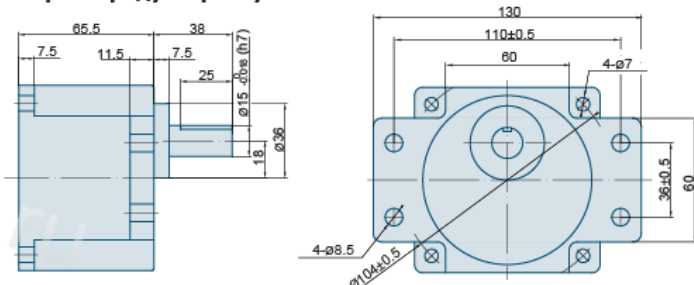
Редукторный электродвигатель Z5D90-24GU
